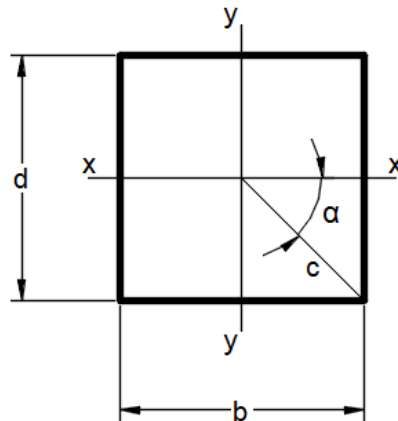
Forma del cordón de soldadura de la base superior del cabezal principal.
